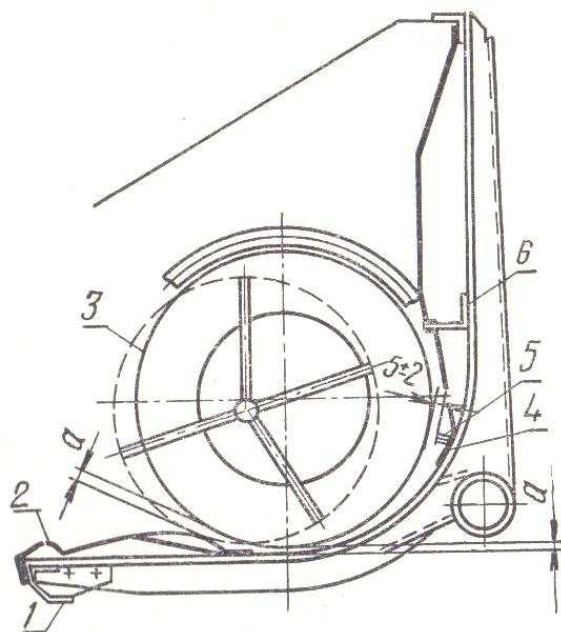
Положение шнека в корпусе жатки комбайна СК-6: 1 – передний брус; 2 – профилированная накладка; 3 – шнек; 4 – нижний отражатель; 5 – регулируемый отсекающий; 6 – верхний отражатель; а – зазоры между шнеком, обшивкой корпуса и передним козырьком
